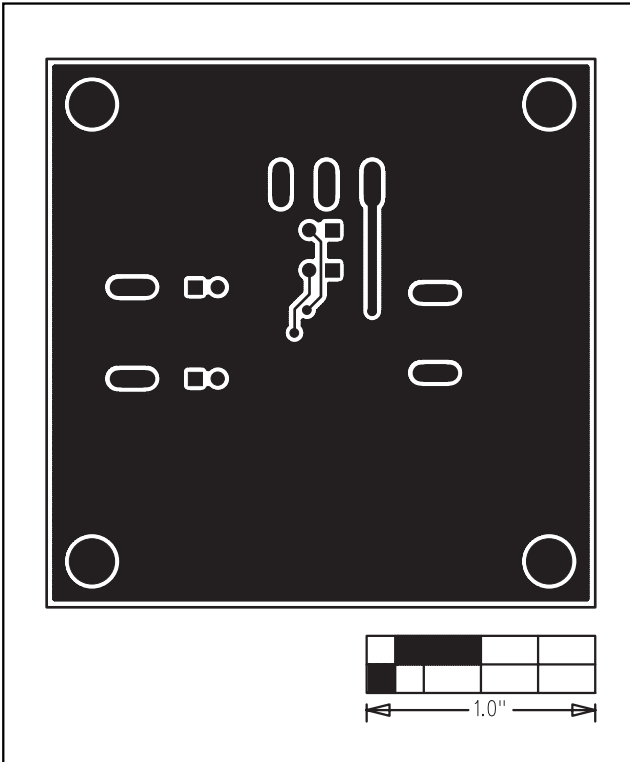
MAX9718A EV 키트 PCB 레이아웃 — 납땜 측
